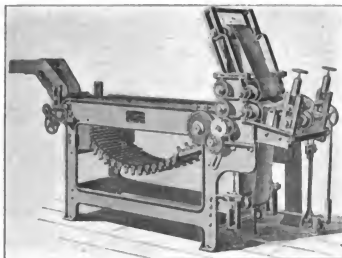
Streckmaschine (drawing frame) der Watson Machine Comp.
